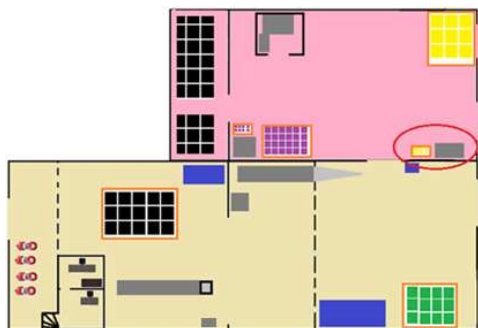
Local onde máquina de corte seria posicionada (2ª proposta de compra de máquina de corte)
